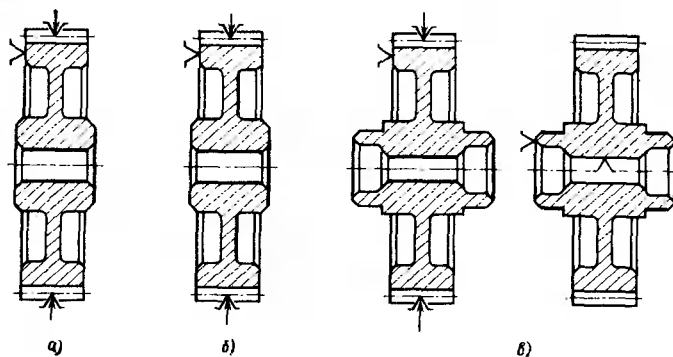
Схема обработки базовых поверхностей заготовки зубчатого колеса после термической обработки:
